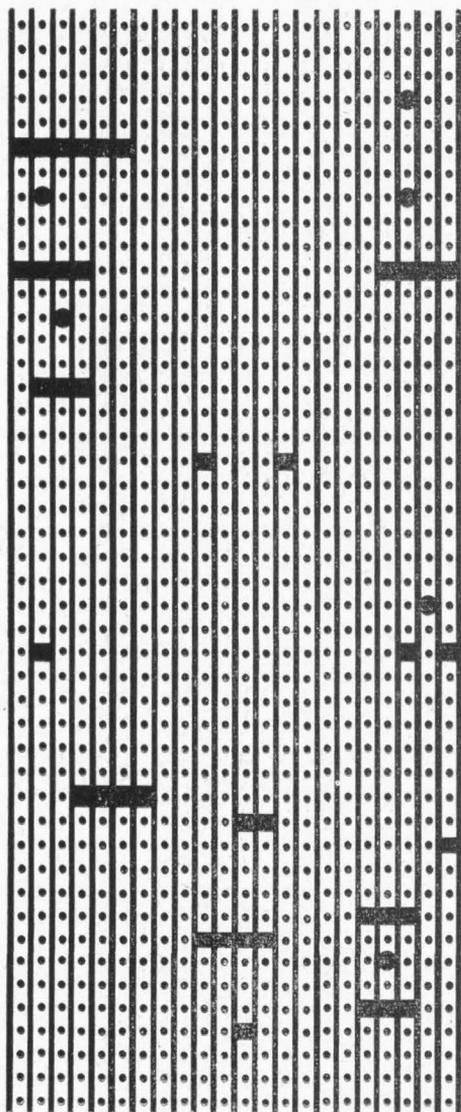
Plaqueta de circuito impresso universal utilizada no protótipo do Autor (face cobreada).
